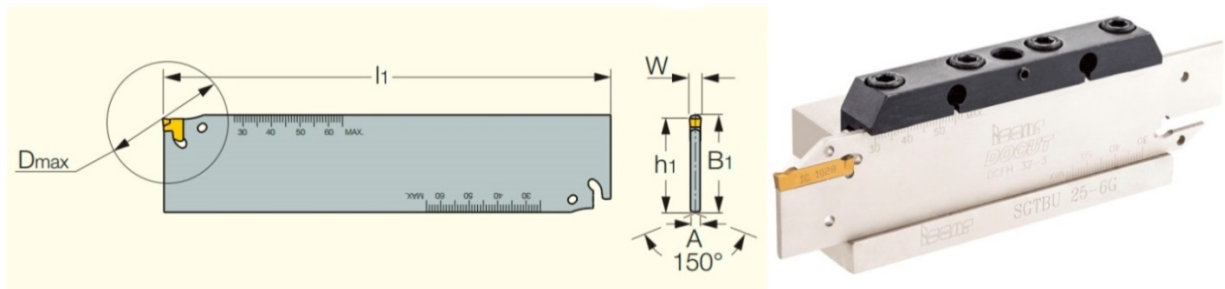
Блок з лезами для обробки канавок та відрізки фірми ISCAR
